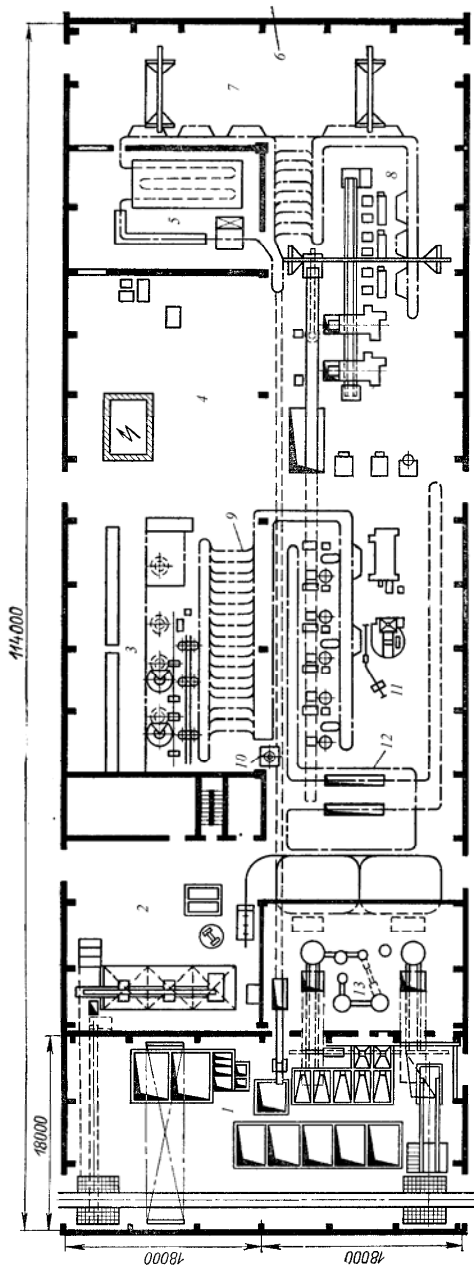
Компонування чавуноливарного цеху виготовлення виливків литтям в оболонковій формі
